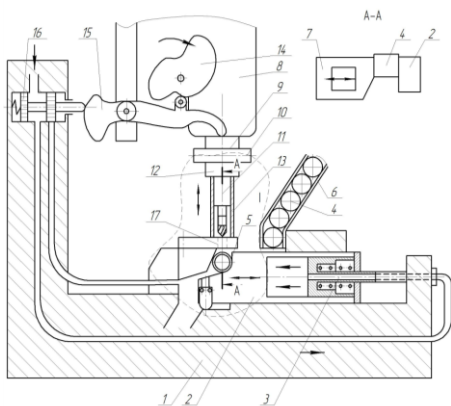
Конструктивна схема пневматичного автоматизованого пристрою для свердління і нарізання різьби в трубчастих заготовках
